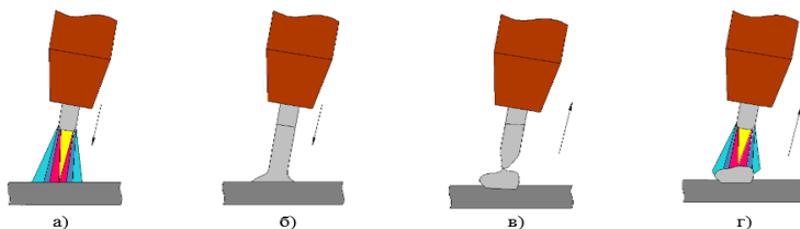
Основной принцип СМТ-процесса: а – дуга горит между проволокой и изделием; б, в – отрыв капли за счет обратного перемещения сварочной проволоки; з – возобновление горения дуги
